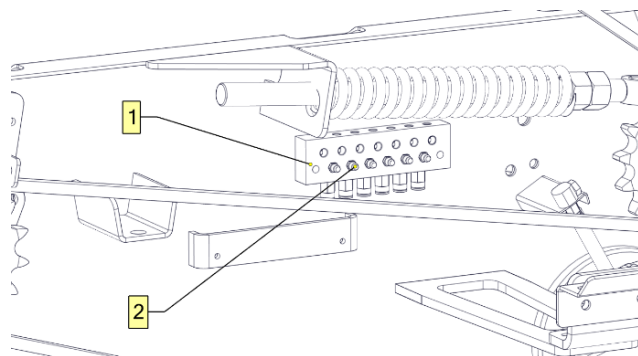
Центральная система смазки подшипников на левой стороне пресс-подборщика
